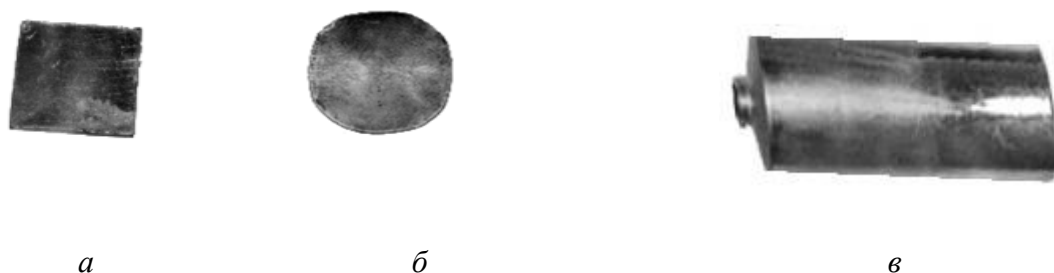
Схема процесу видавлювання тюбика з квадратної заготовки за три переходи:
